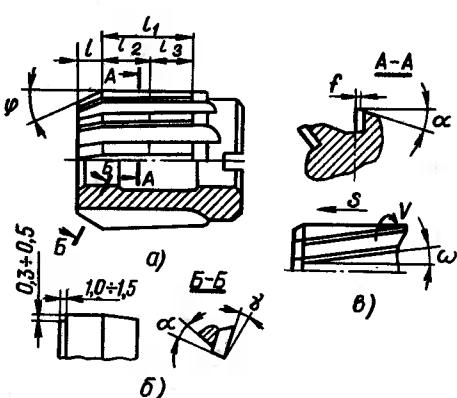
Насадная развертка с твердосплавными пластинами
